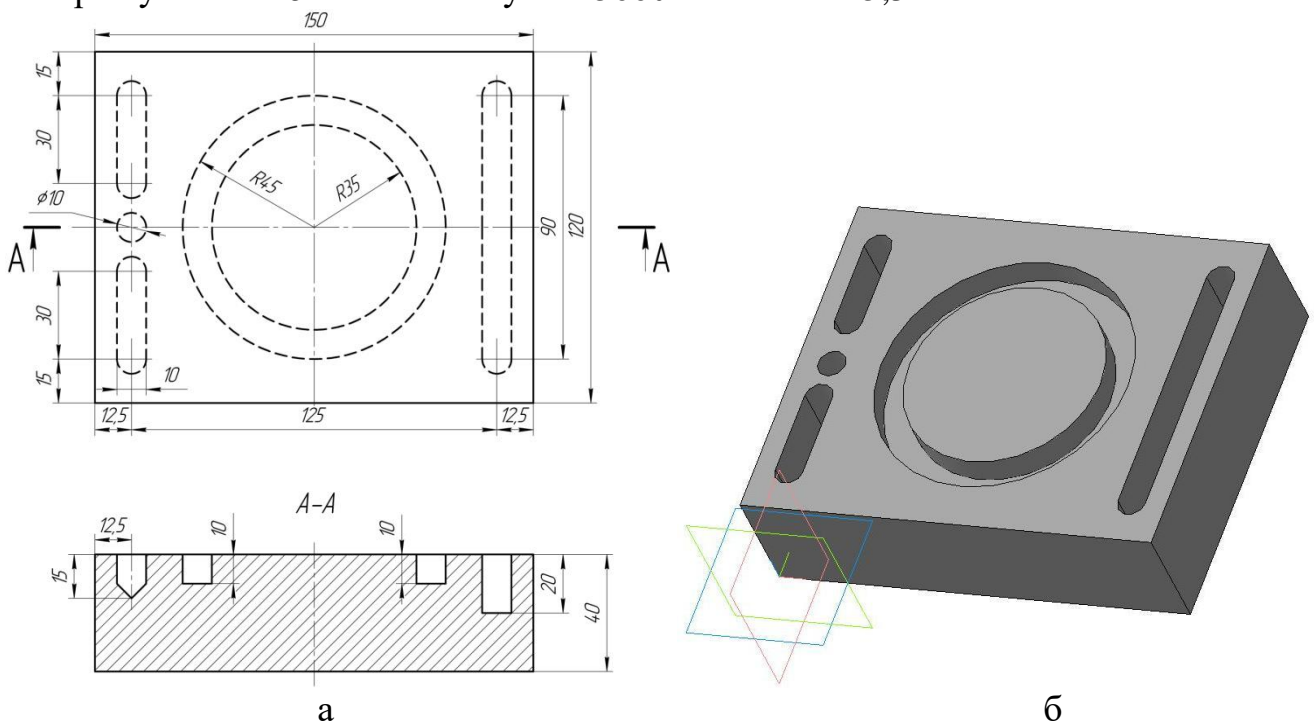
Креслення деталі (а) та 3D модель деталі після обробки
